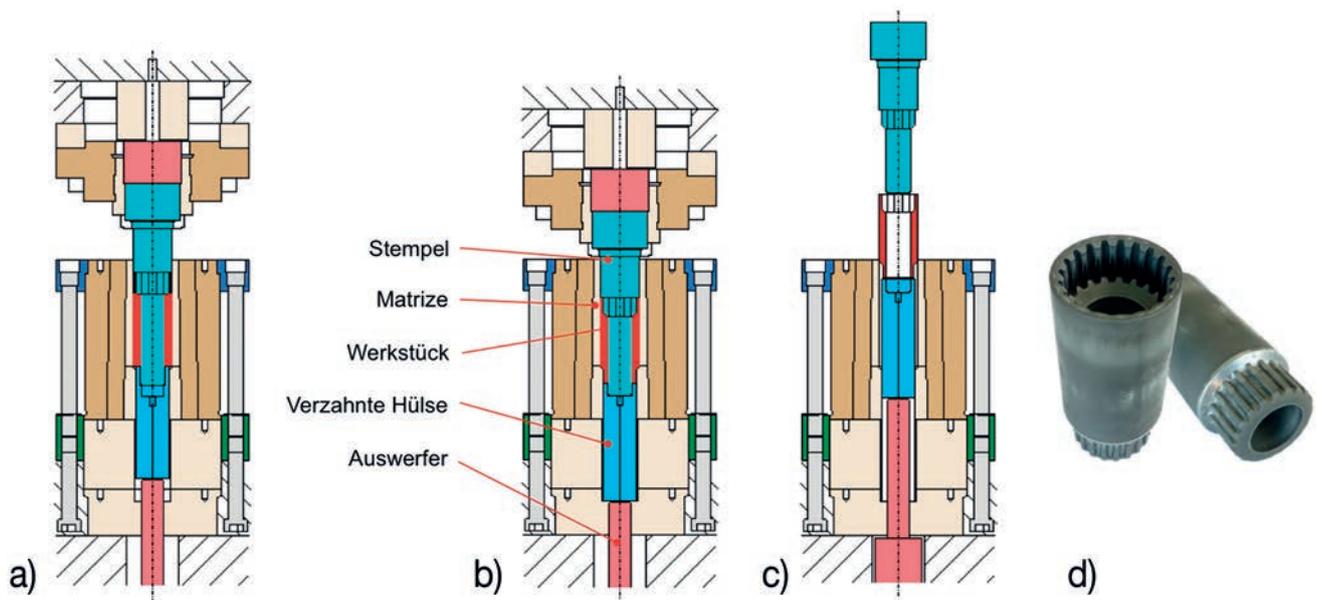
Versuchswerkzeug für das kombinierte Hohl-Vorwärts- und Hohl-Rückwärts-Fließpressen in typischen Prozessstadien: a) Aufsetzen des Stempels, b) Endstadium des Pressens, c) Auswerfen und d) erzeugte Pressteile. Bilder: Autoren
